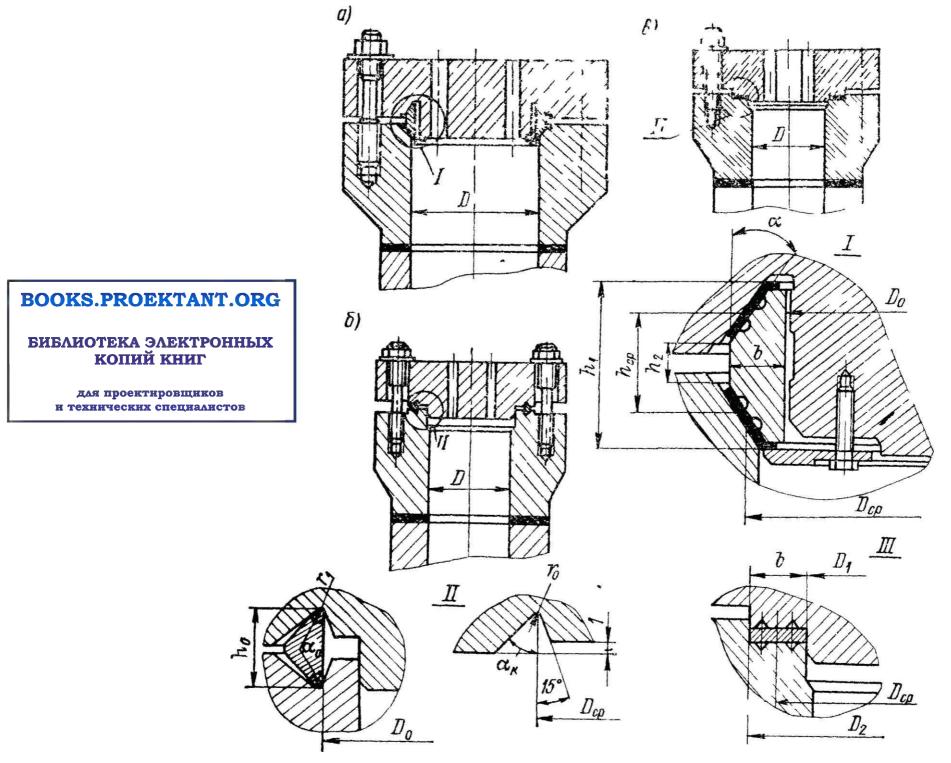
Конструкции затворов a — с двухконусным обтюратором, b — с дельта-обтюратором; b — с плоской металлической прокладкой
